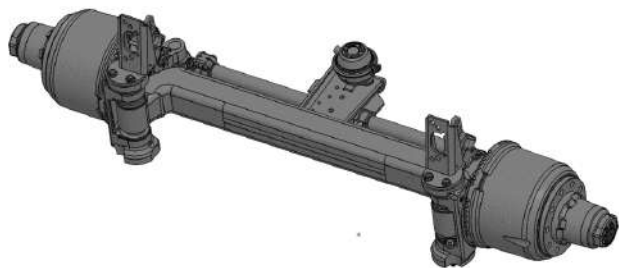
Самоустанавливающийся (свободно-поворотный) осевой агрегат
